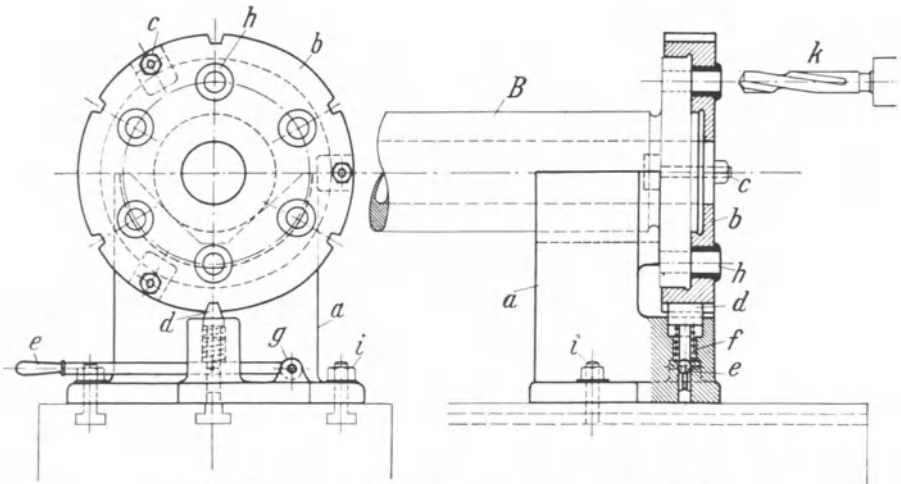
Bohrplatte mit Teilvorrichtung für schwere Flanschwellen.
